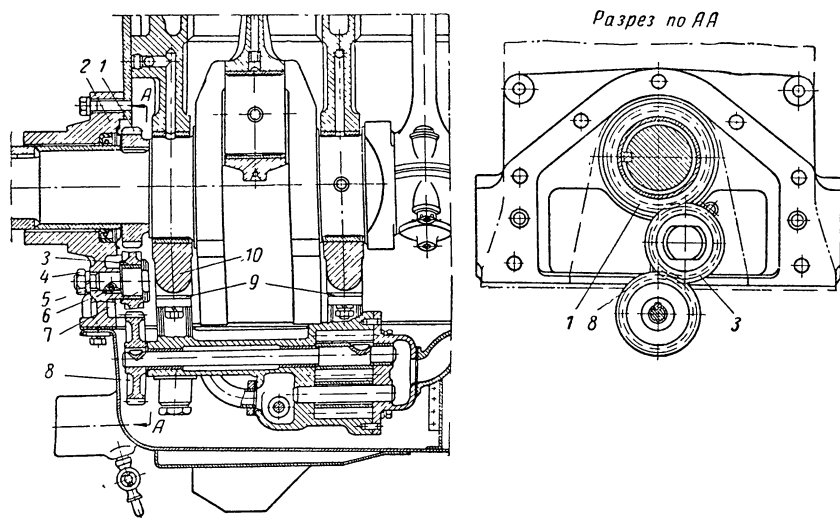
Масляный насос; 1 — шестерня привода масляного насоса; 2 — предохранительный клапан; 3 — масляный насос; 4 — шестерня привода масляного насоса; 5 — предохранительный клапан; 6 — перепускной клапан.
